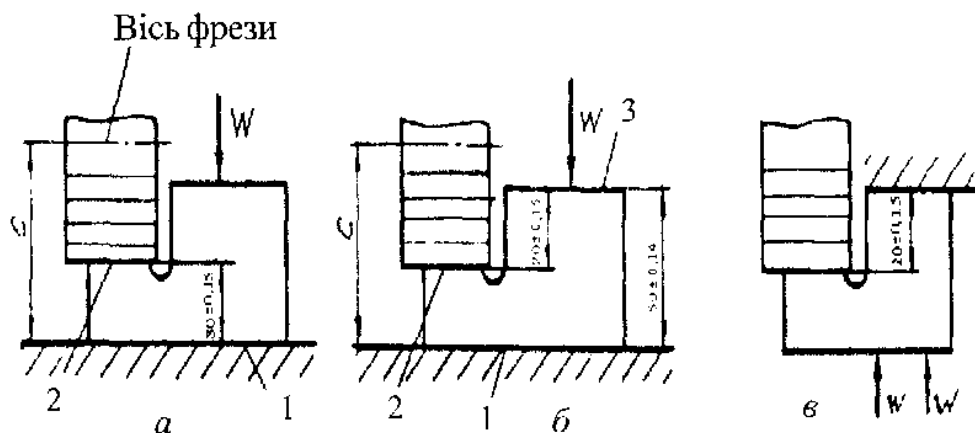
Схеми для розрахунку похибки базування при встановленні заготовок на площину
